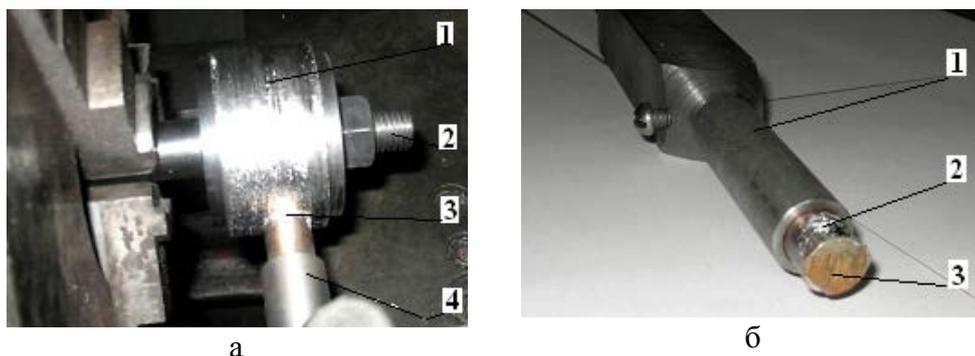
Элементы процесса формирования покрытия на образцах: а - установка образца-шейки на оправку: 1- образец-шейка; 2 - оправка; 3 - галлиево-индиевая среда; 4 - корпус устройства; б - устройство для нанесения покрытия; 2 - следы галлиево-индиевой среды на инструменте-цилиндре; 3 - инструмент-пруток (материал БрОФ4-0,25)
